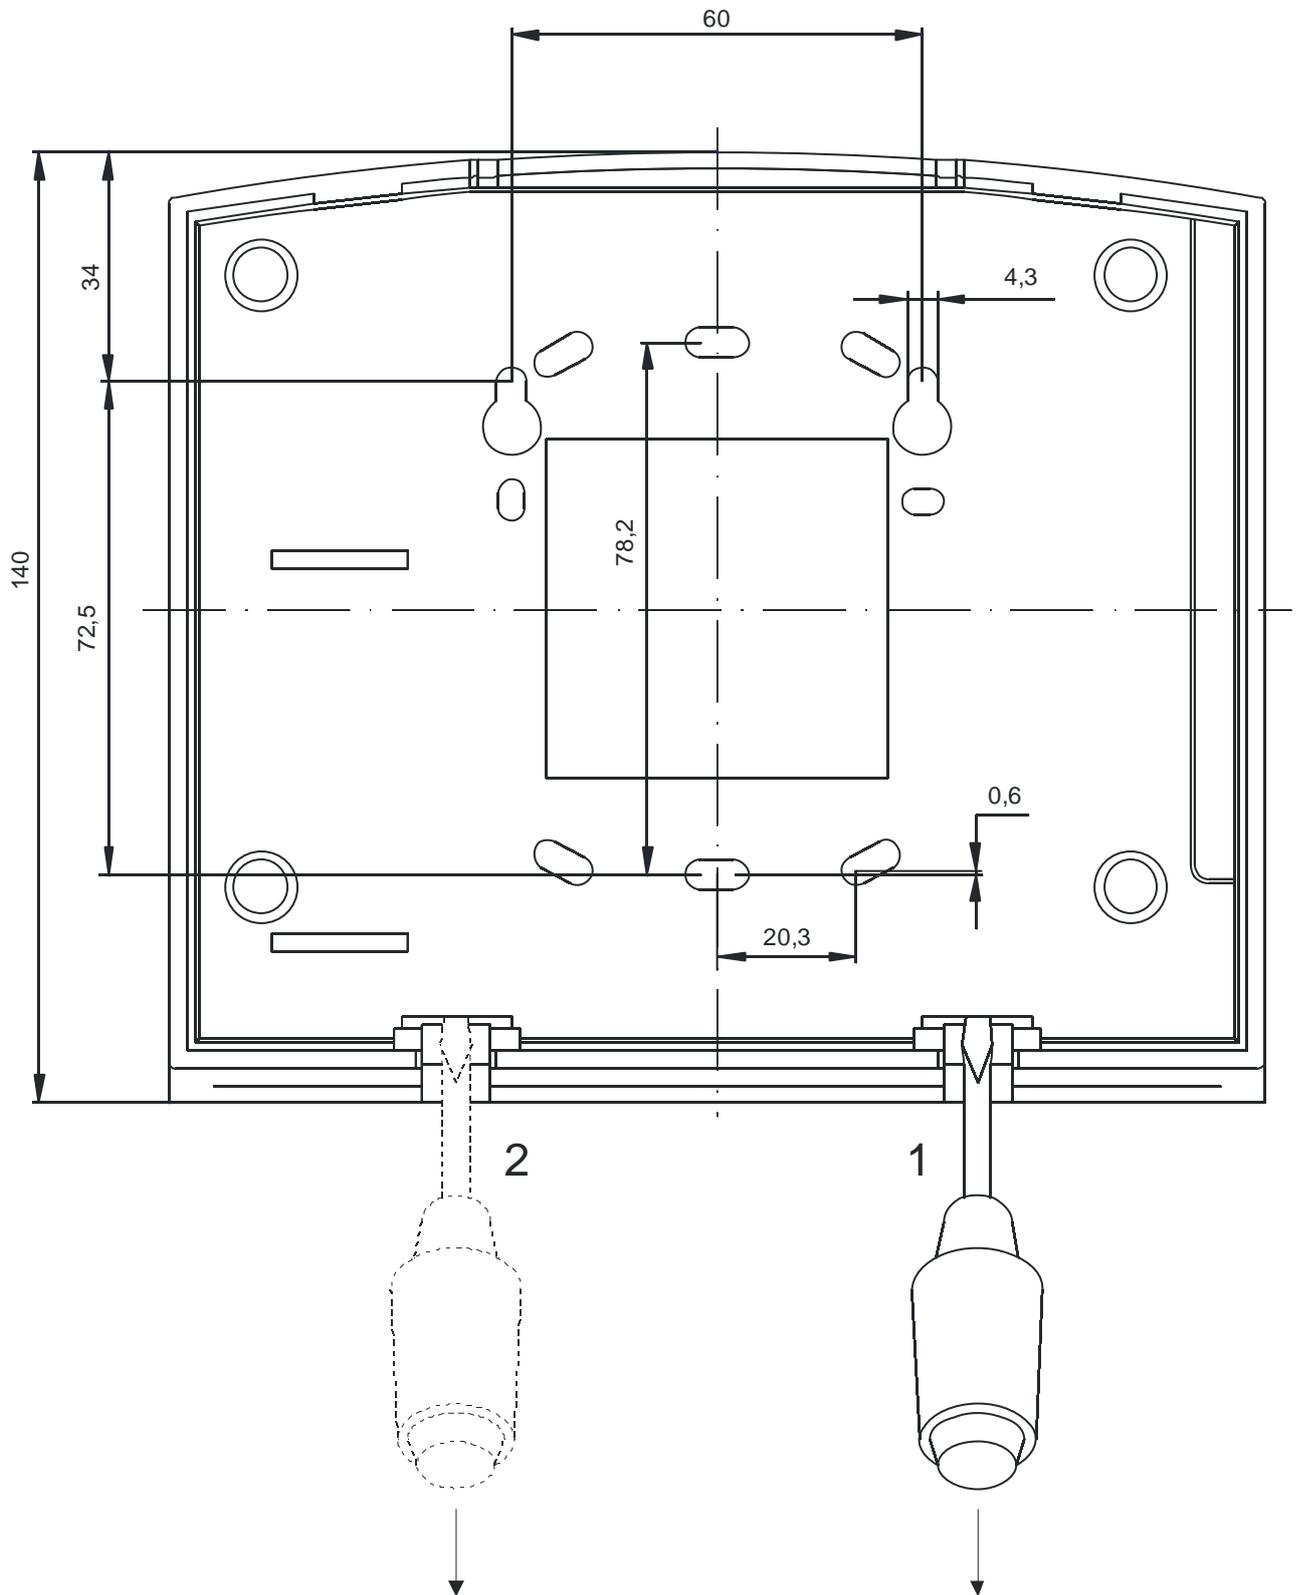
Чертеж отверстий в корпусе для крепления пульта (вид сзади).
